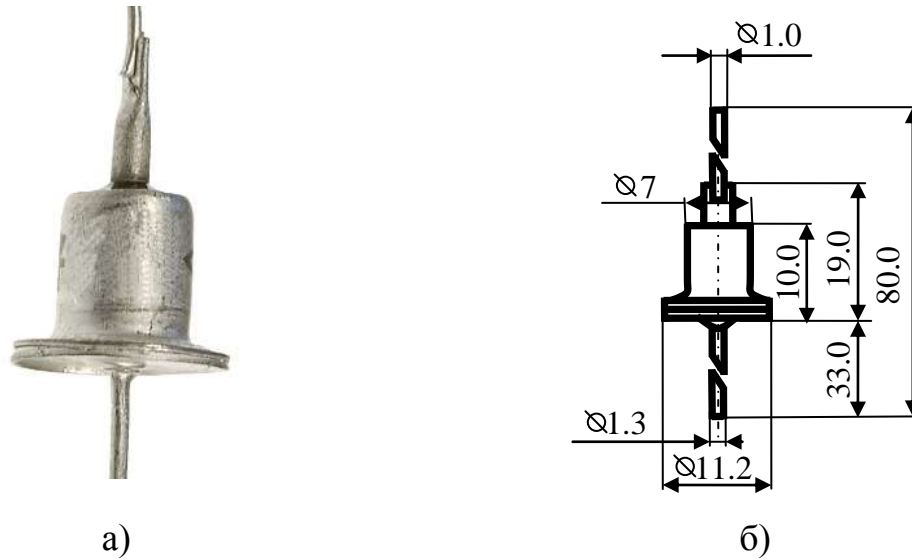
Діод Д226Б: а) зовнішній вигляд; б) габаритне креслення
